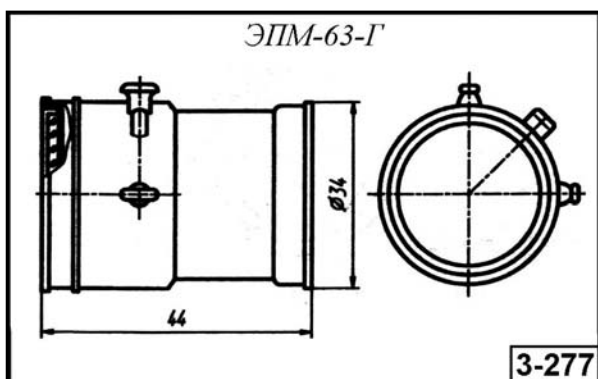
Внешний вид и габаритные размеры преобразователя ЭПМ-63Г
